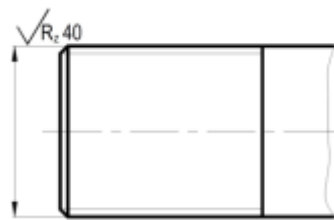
Обозначение шероховатости поверхности профиля резьбы
